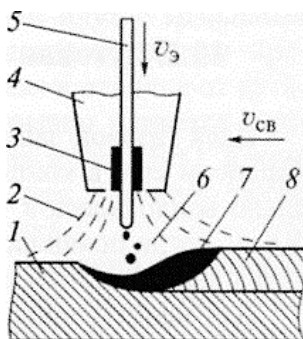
Схема струйной газовой защиты металла при сварке:
